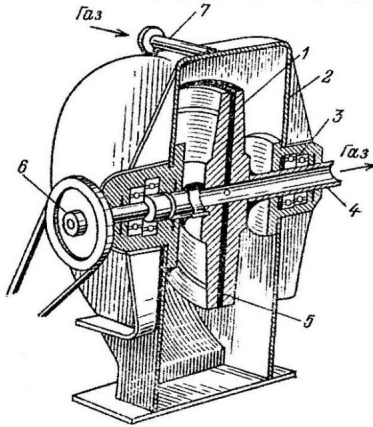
Роторний пиловловлювач ЦРП: 1 – ротор; 2 – корпус; 3 – опора; 4 – полий вал; 5 – радіальний канал; 6 – шків; 7 – патрубок
